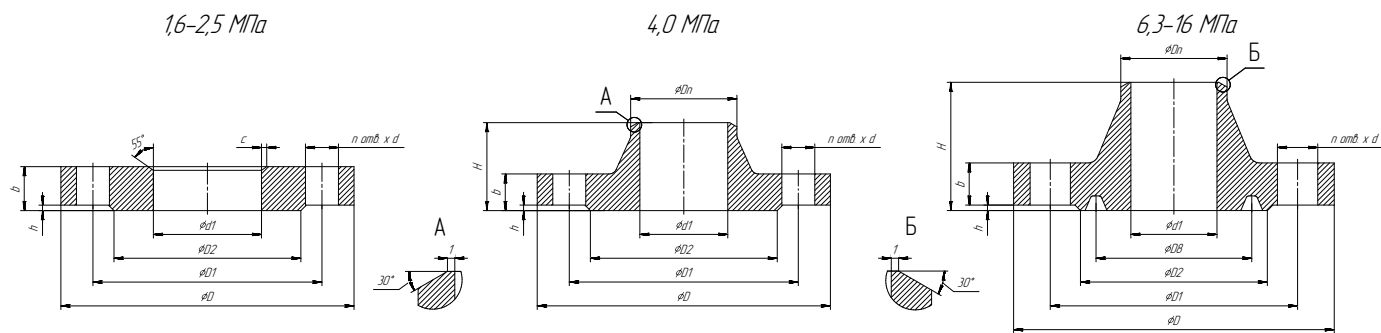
Присоединительные размеры фланцев расходомера и КМЧ
